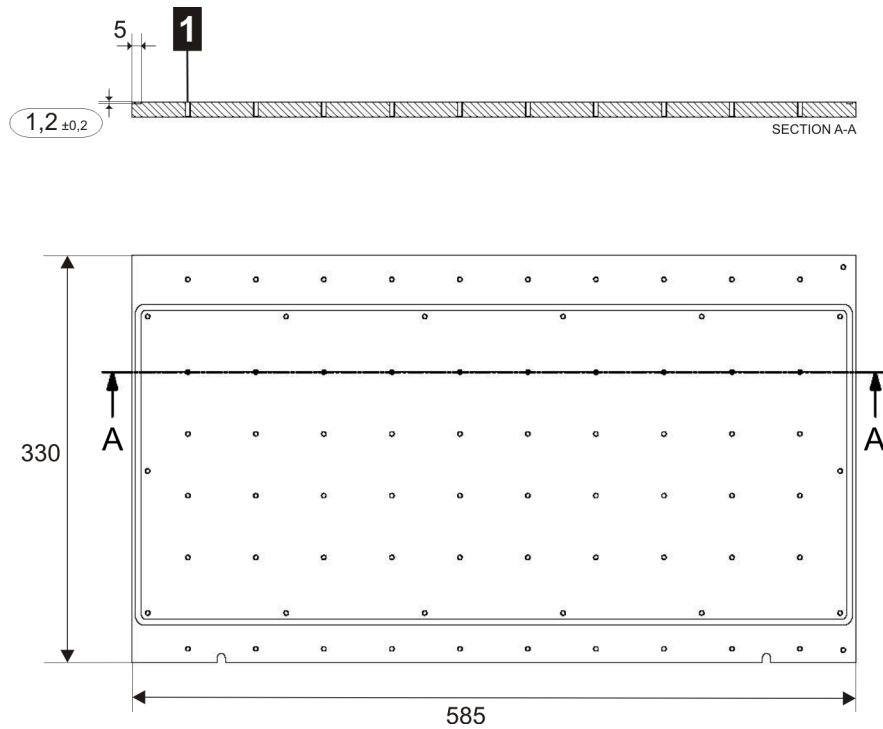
Abmessungen Kühlplatte D3-XM 300-060, Maße in mm
